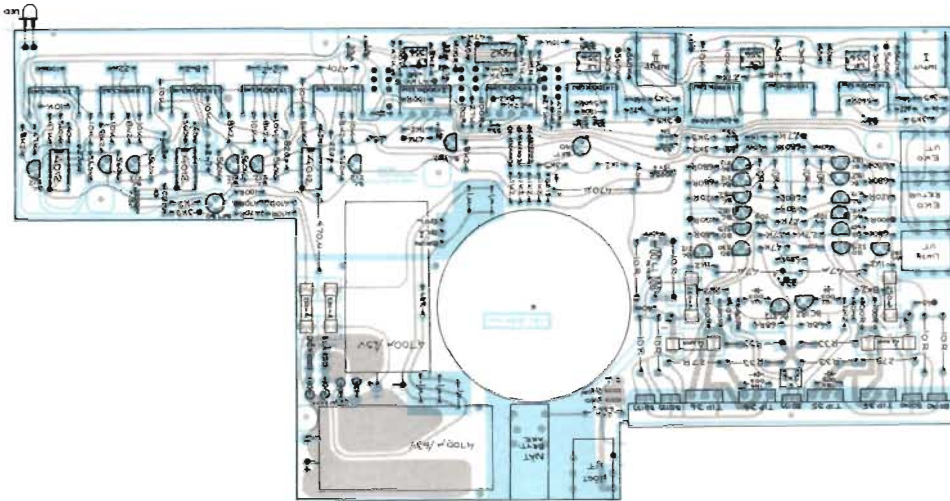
Komponenternas placering på det dubbelsidiga kretskortet.
